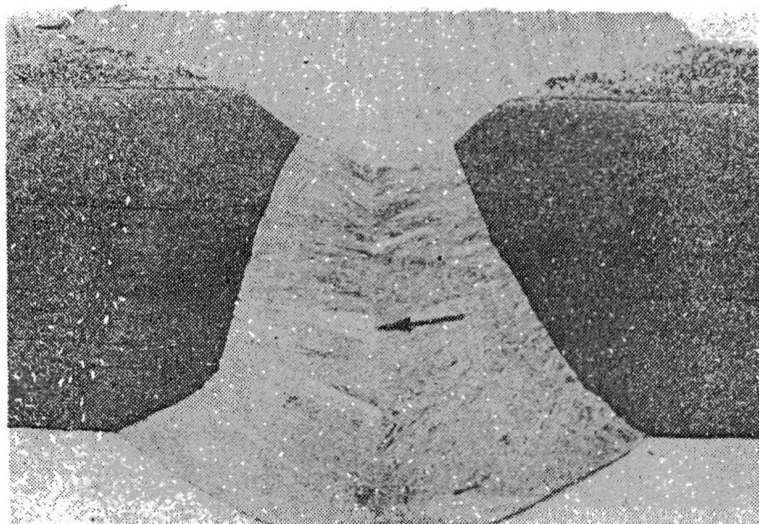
При автоматической дуговой сварке двухслойной стали Ст.3сп+12Х18Н10Т проволокой Св-05Х30Н40М6ТБ под флюсом АН-26, травление в реакторе № 5 (см. табл. 1), 3<sup>х</sup>
